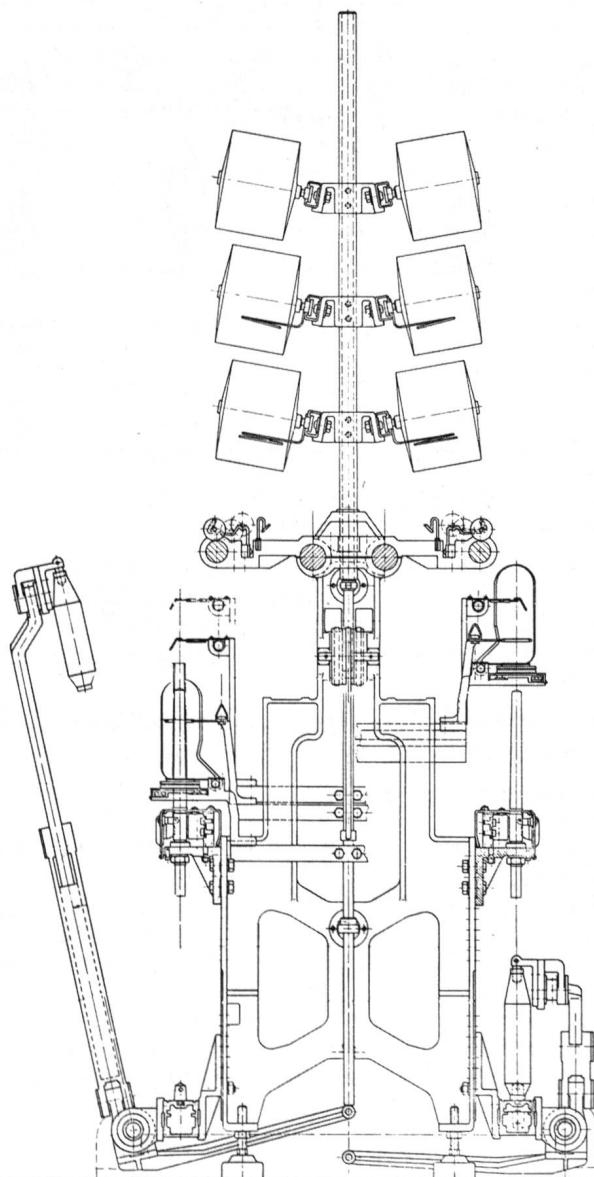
Querschnitt Ringzwirnmaschine «Zinser»
